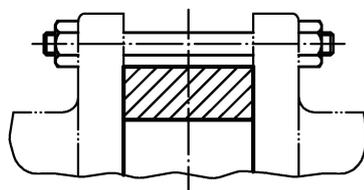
Gehäuse zum Einklemmen ohne Flansch
